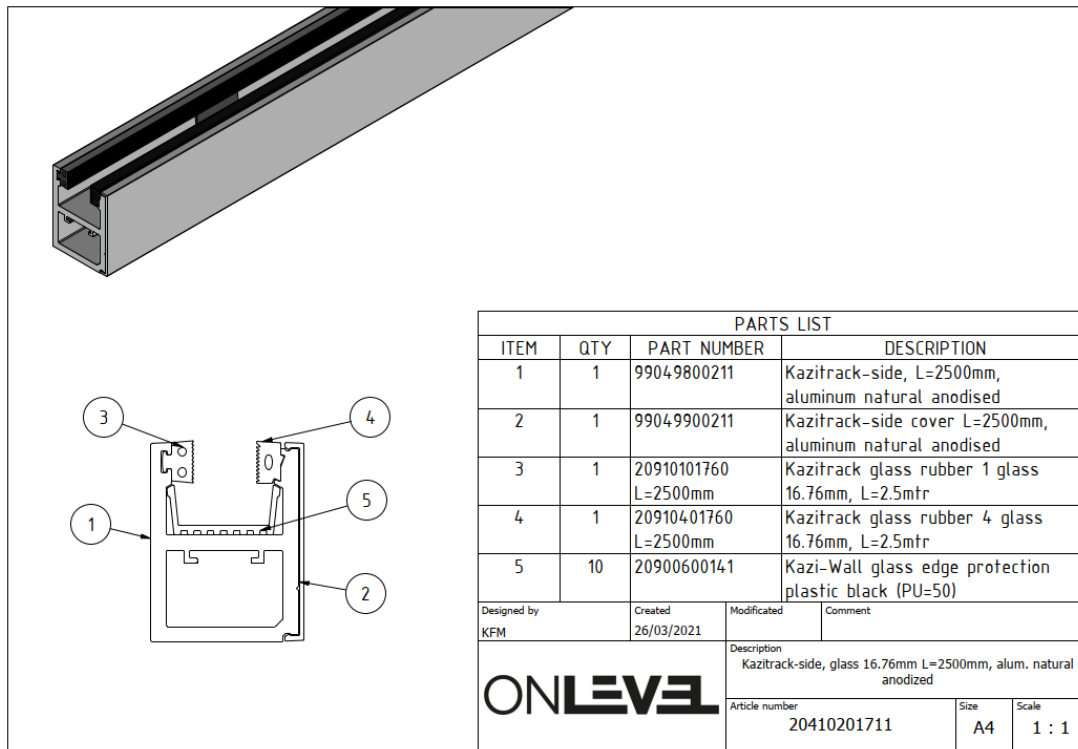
1teiliges Profil, L=2.500 mm für Glasstärke 16,76 und 17,52 mm
